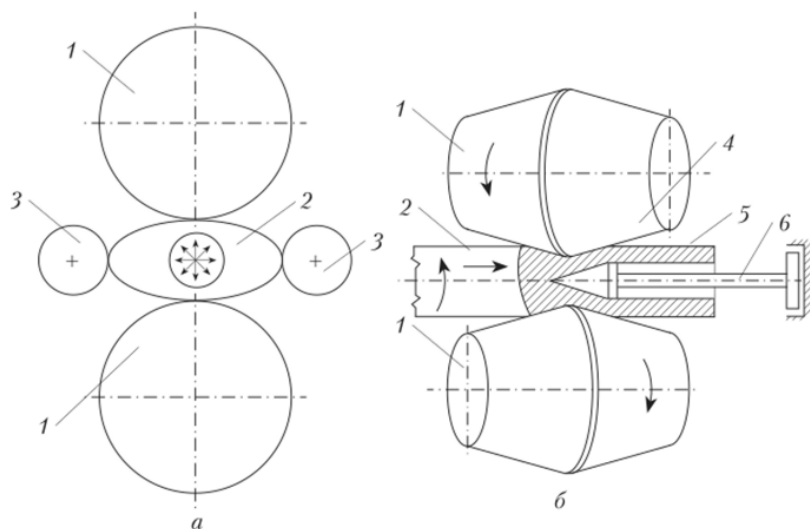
Поперечно-винтовая прокатка заготовки трубы (гильзы) [1]:
